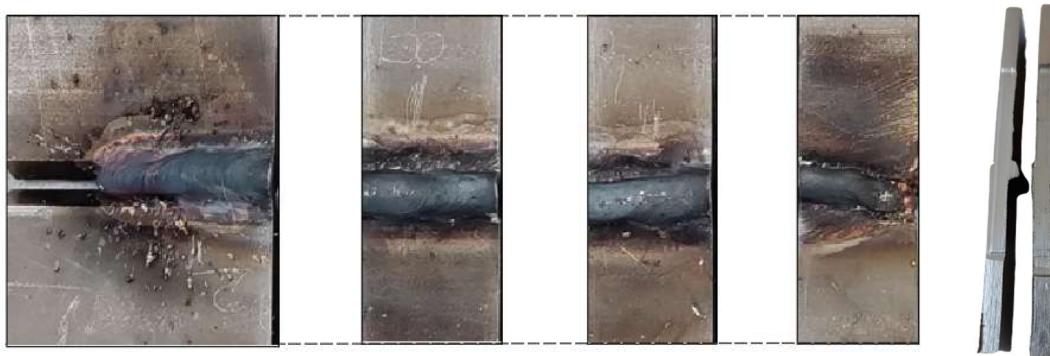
Cordão de soldadura e secção transversal dos provetes da amostra B.
